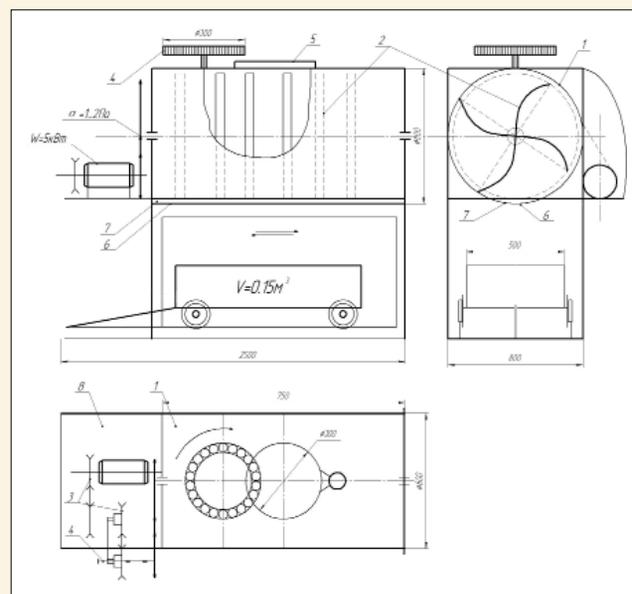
Конструктивная схема установки для инокуляции компоста биопрепаратами: 1 – барабан смесительный; 2 – ротор-смеситель; 3 – механизм привода; 4 – дозатор; 5 – люк загрузочный; 6 – заслонка шиберная; 7 – окно загрузочное; 8 – рама установки
